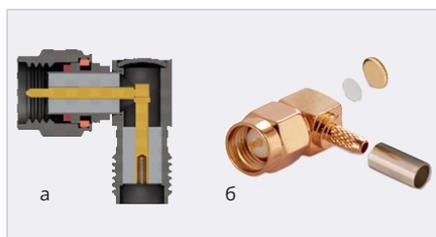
Схематическое изображение соединителей первого конструктивного исполнения (а), внешний вид соединителя S-121L (б)
